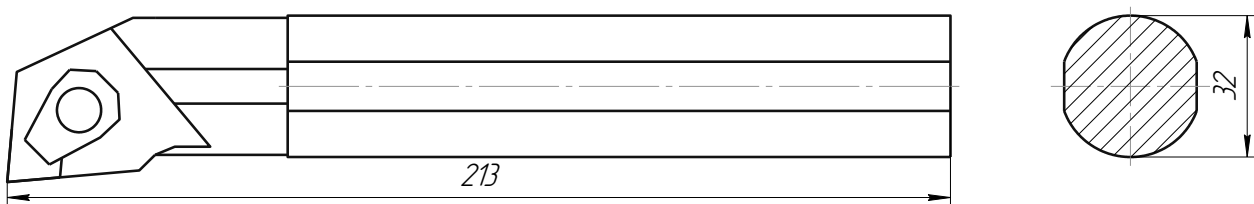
Расточной токарный резец марки S32X-MCLNL 12-Bh 12
